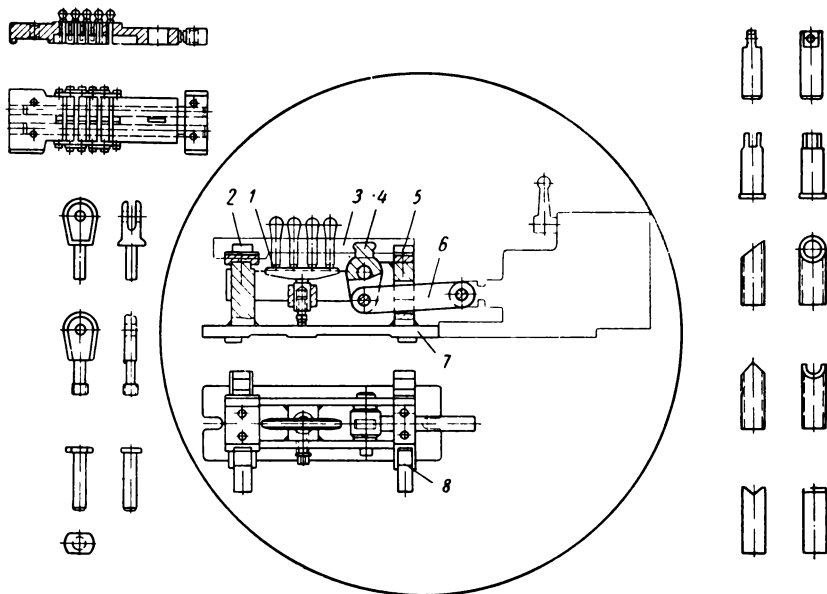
Универсальное наладочное приспособление для фрезерования нормалей
